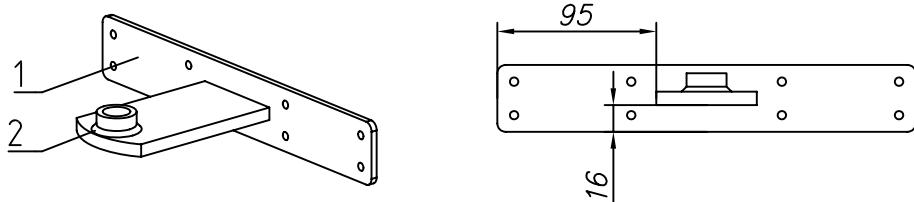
Изготовление кронштейна для крепления электропривода
